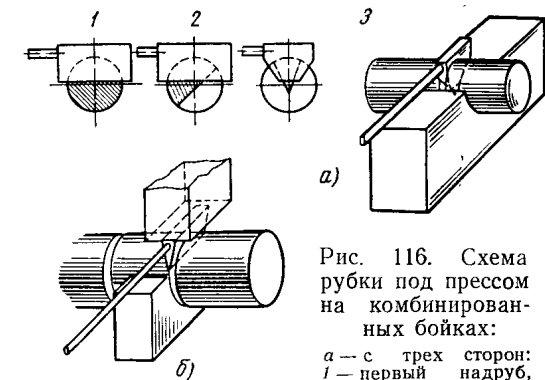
Схема отрубki под прессом на комбинированных бойках:
